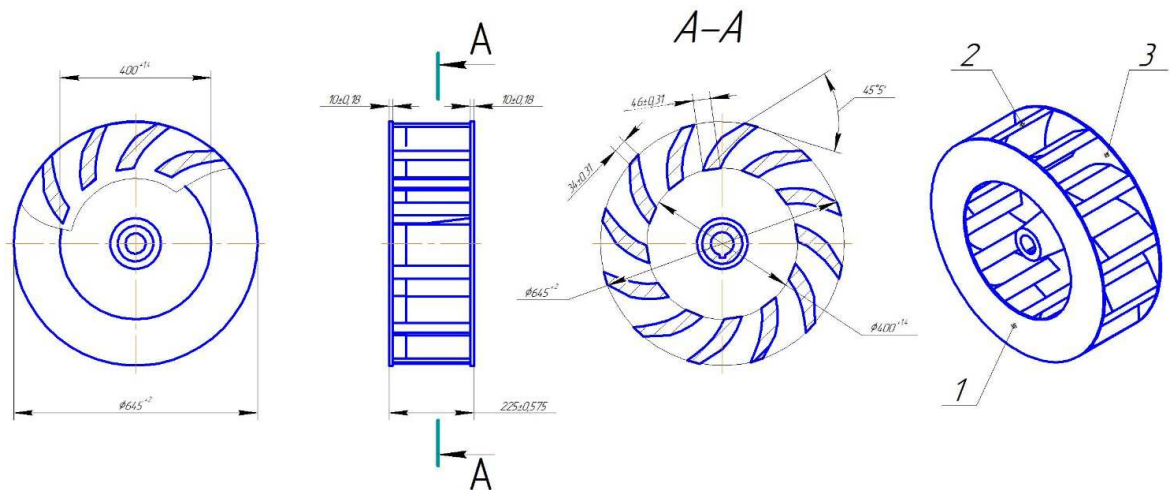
Ескіз рабочего колеса вентилятора:
